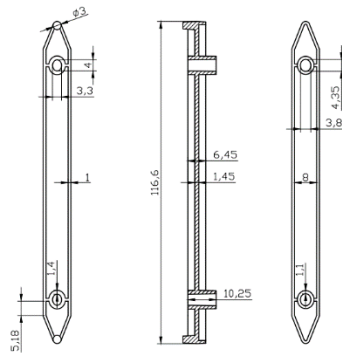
Dimensiones pieza 1. Fuente: elaboración propia.
